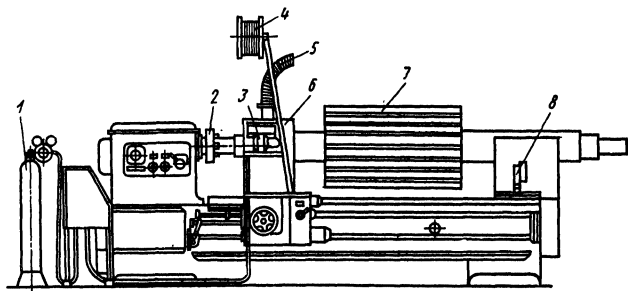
Установка для нанесения покрытий газоплазменным напылением
